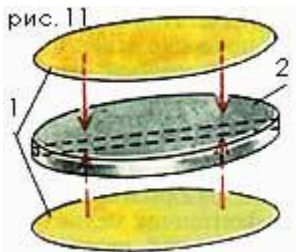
Изготовление корпуса девона из расплющенной "оливки": 1 - латунь или мельхиор; 2 - свинец.
